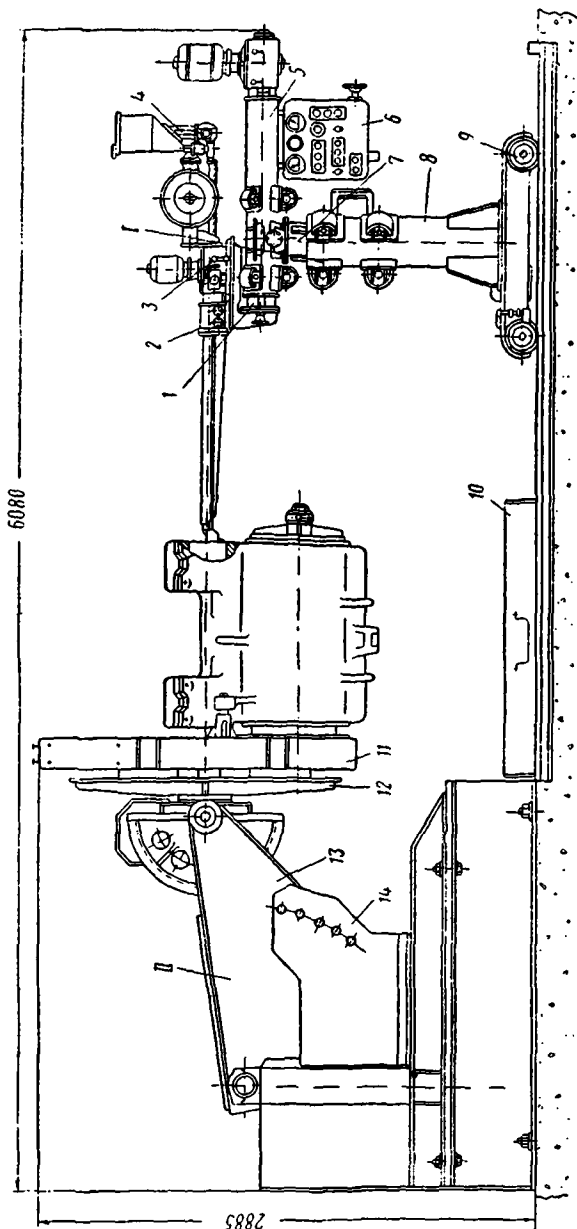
Установка для автоматической накладки под слоем флюса остонов тяговых двигателей:
